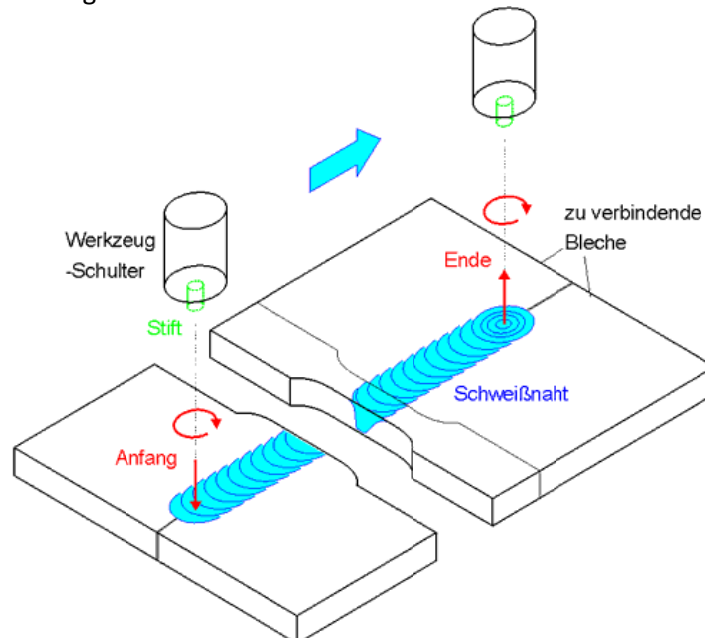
Rührreißschweißen- Entnahme der Zugprobe[80]
